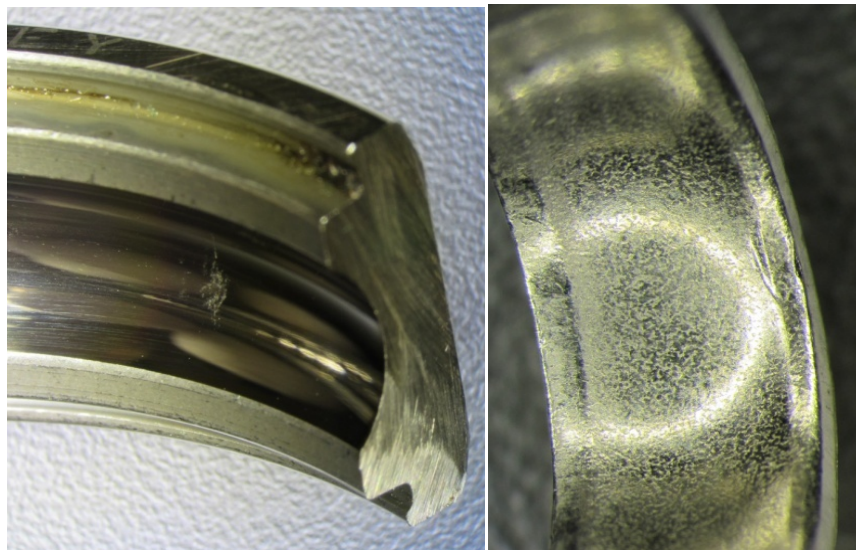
Обнаруженные дефекты подшипника качения
